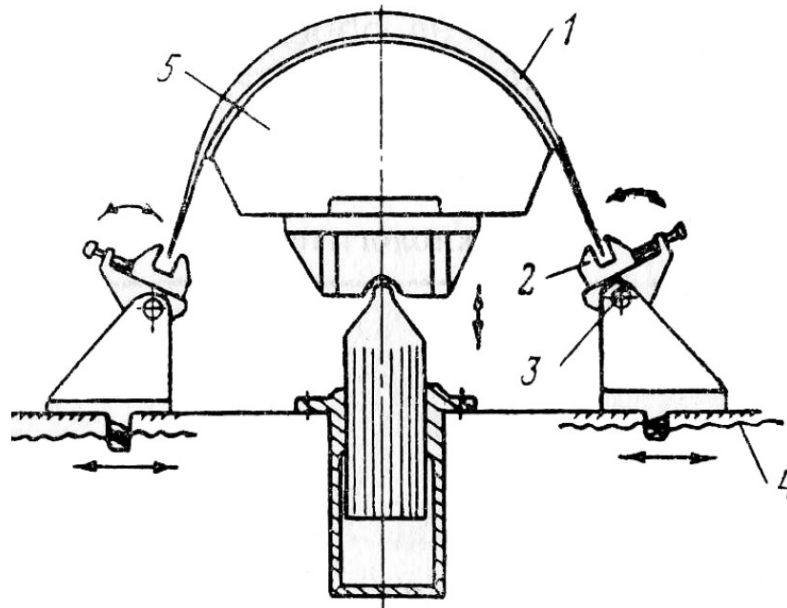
Схема обтяжного пресу типу ОП-3
